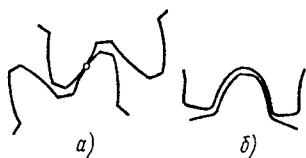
Зацепление зубчатых колес с эвольвентным (а) и круговым (б) профилями зубьев
